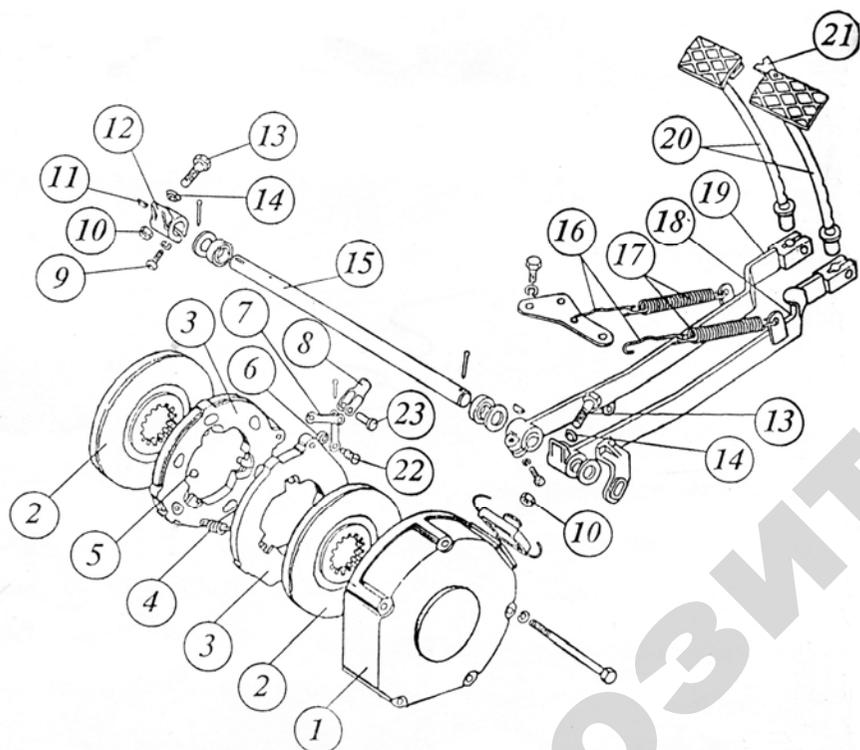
Рабочий тормоз и управление трактора «Беларус-1221»: 1 – кожух; 2 – диски тормозные; 3 – диски нажимные; 4 – пружина стяжная; 5 – шарик; 6 – гайка; 7 – тяга; 8 – вилка; 9 – болт; 10 – контргайки; 11 – шпонка; 12 – рычаг; 13 – болты регулировочные; 14 – шайбы сферические; 15 – валик; 16 – скоба; 17 – пружина стяжная; 18, 19 – рычаги; 20 – стержень с подушкой (педаля); 21 – стопорная планка; 22 – болт; 23 – палец
